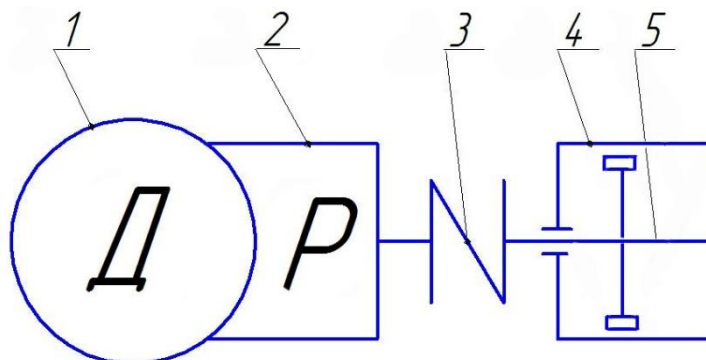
Кінематична схема приводу лопатевого валу стерилізатора: 1 - електродвигун; 2 - адаптер мотор-редуктора; 3 - муфта; 4 - корпус; 5 - лопатевий вал.
